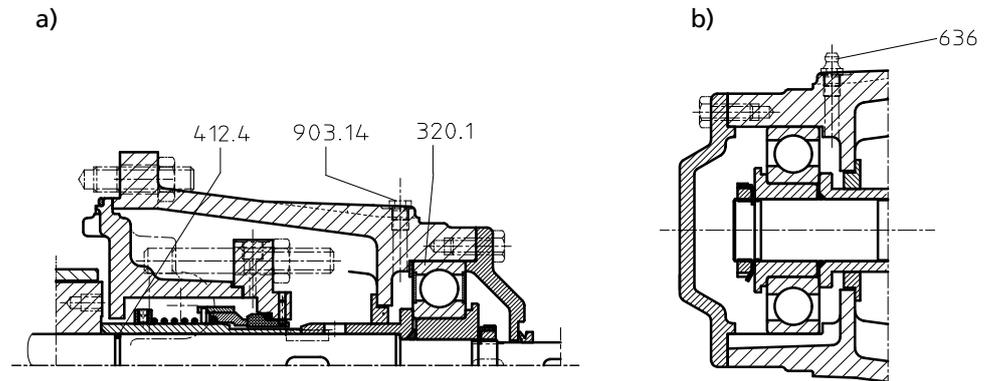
а) Подшипник со стороны привода Multitec 32 - б) Смазка консистентной смазкой через смазочный ниппель с противоположной приводе стороны, типоразмеры 100 и 125
